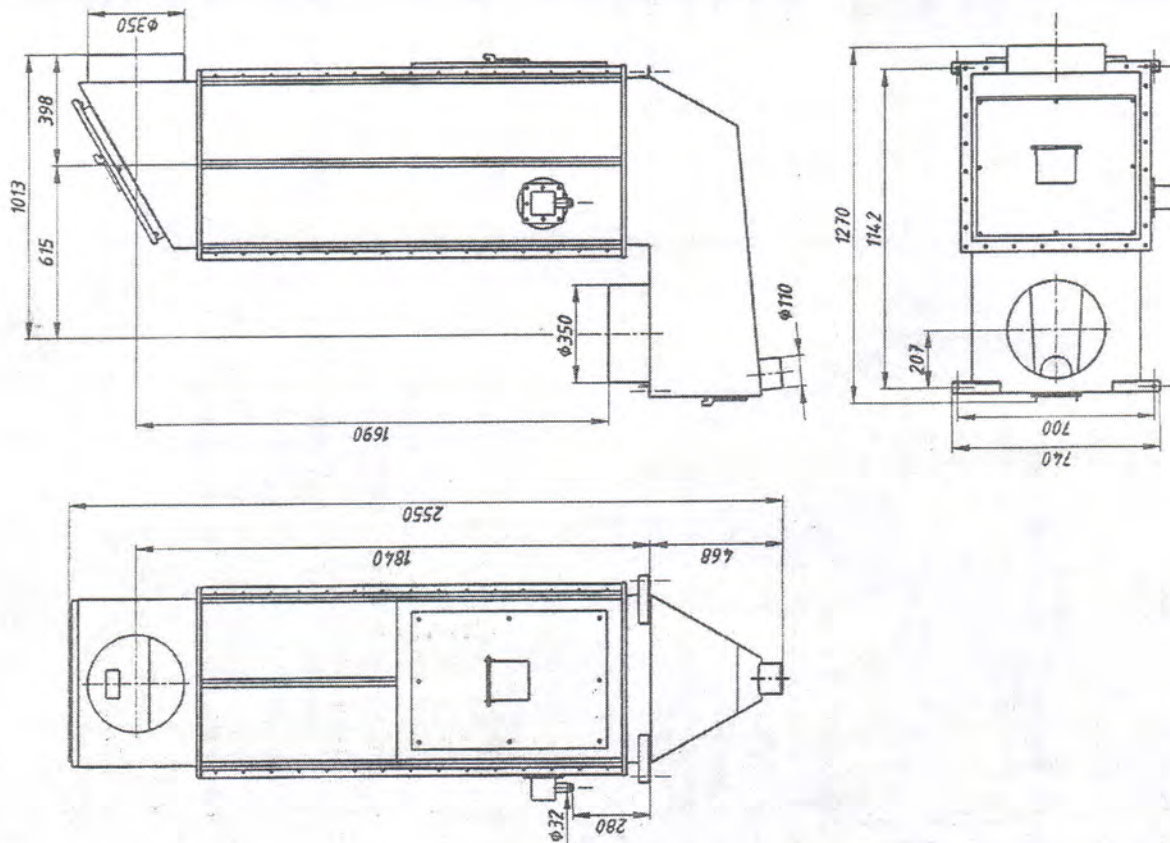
Габаритные, присоединительные и посадочные размеры ВГЖР-6
